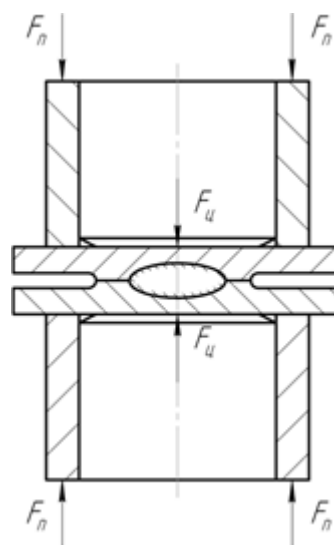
Схема обтискання деталей при прецизійному електроконтактному точковому зварюванні
